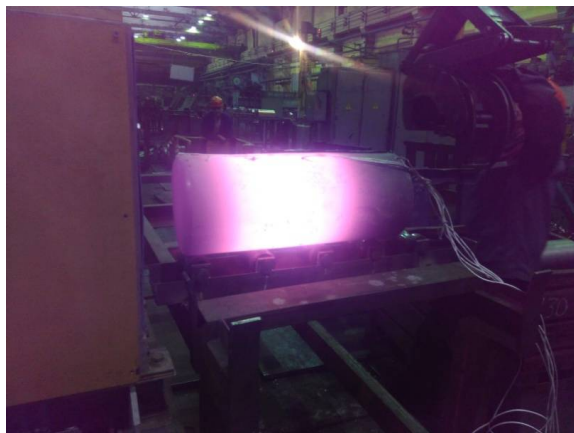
Заготовка после нагрева при закороченных боковых витках
